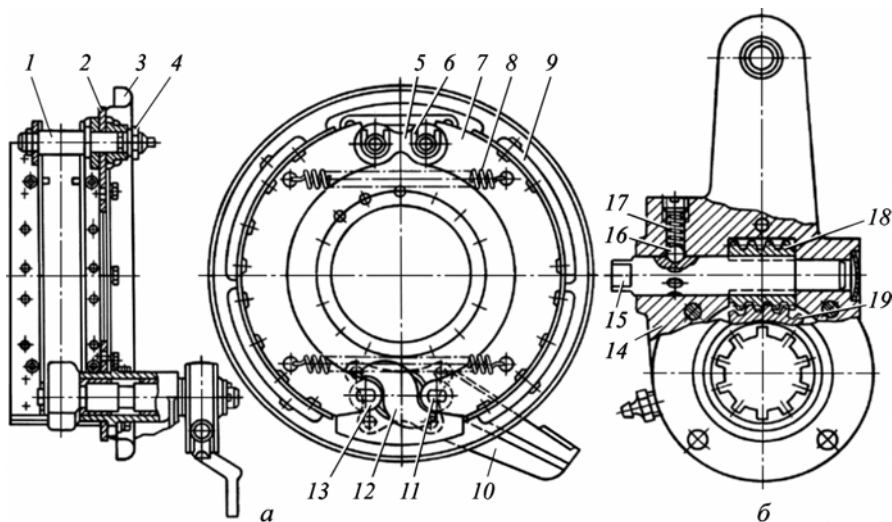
Колісний гальмовий механізм (а) та регулювальний важіль (б) автомобіля КАМАЗ-5320:
